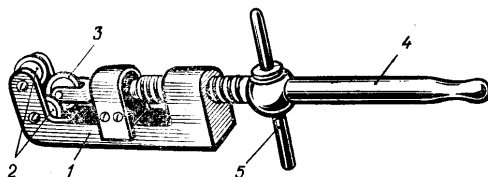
Труборез: 1 – скоба; 2 – неподвижные ролики; 3 – подвижный ролик; 4 – рукоятка; 5 – вороток
